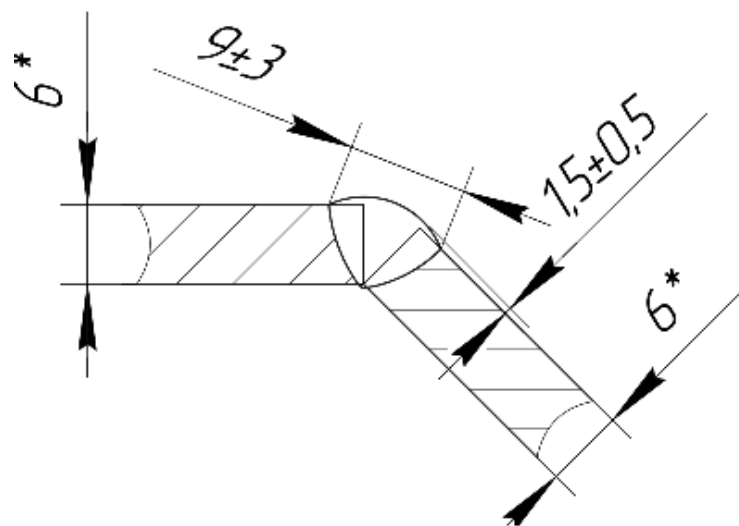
Конструктивные элементы сварного шва У2 ГОСТ 23518-79
